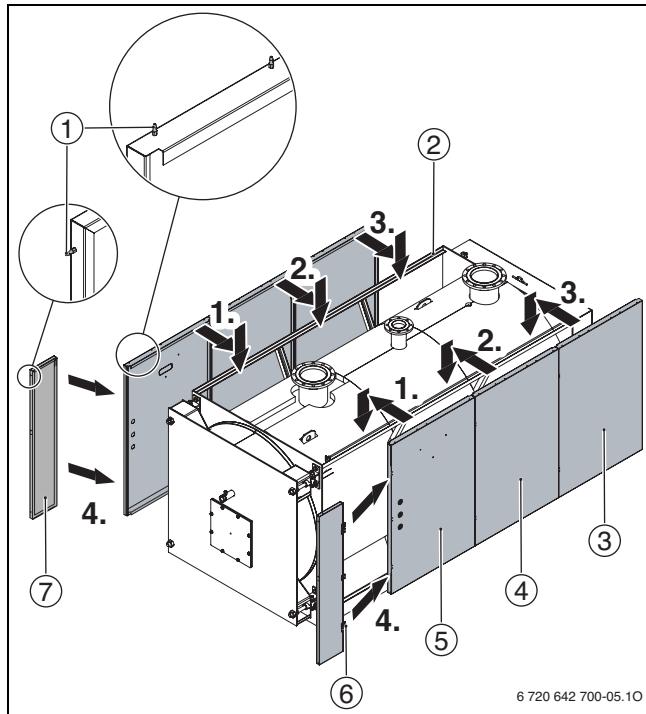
Монтаж боковых стенок в котлах 1400 - 1850 кВт
